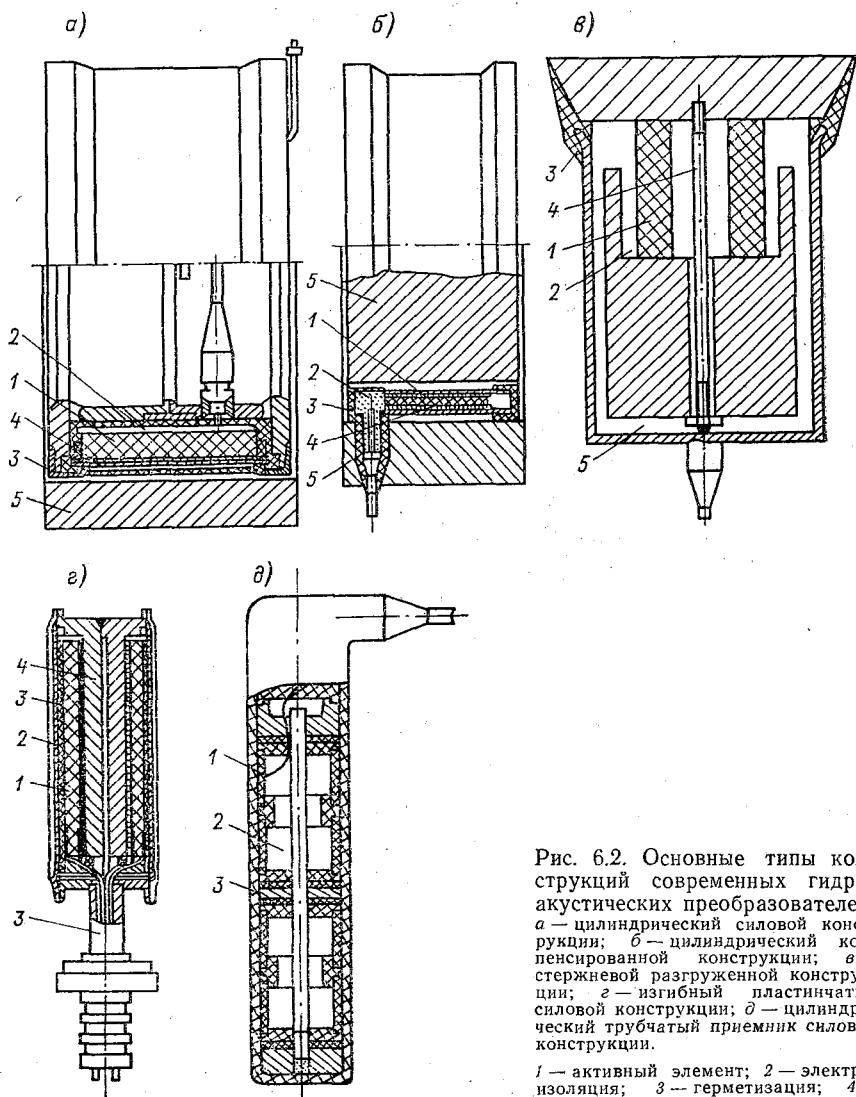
Основные типы конструкций современных гидроакустических преобразователей. а — цилиндрический силовой конструкции; б — цилиндрический компенсированной конструкции; в — стержневой разгруженной конструкции; г — изгибный пластинчатый силовой конструкции; д — цилиндрический трубчатый приемник силовой конструкции.
